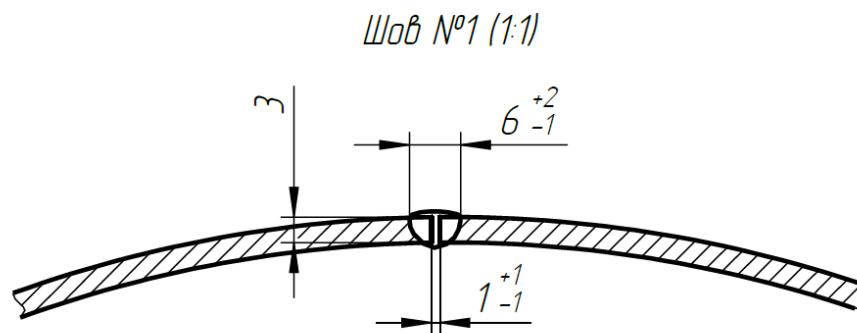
Детальне зображення стикового поздовжнього шва обичайки №1
